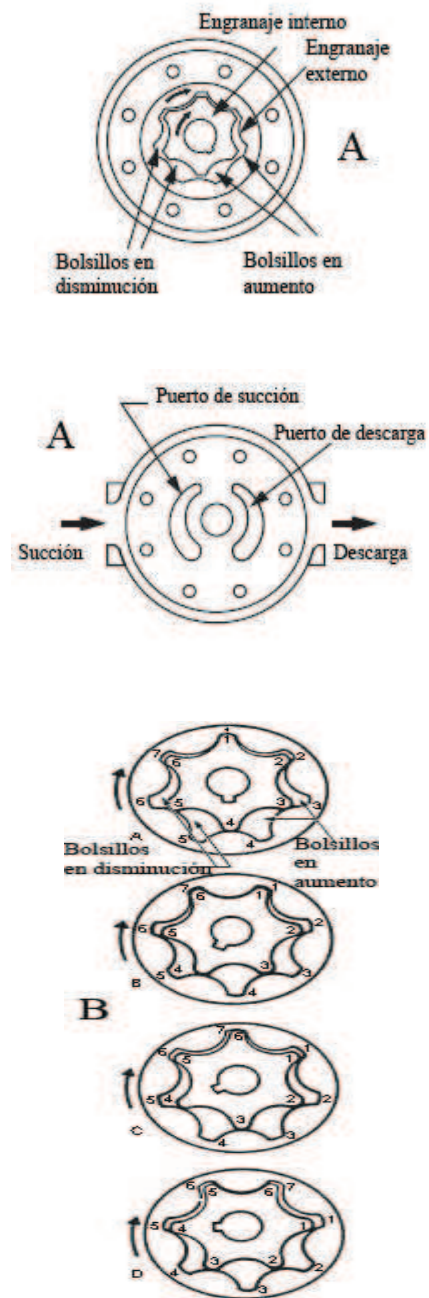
Bombas de engranajes internos(vistas laterales)
